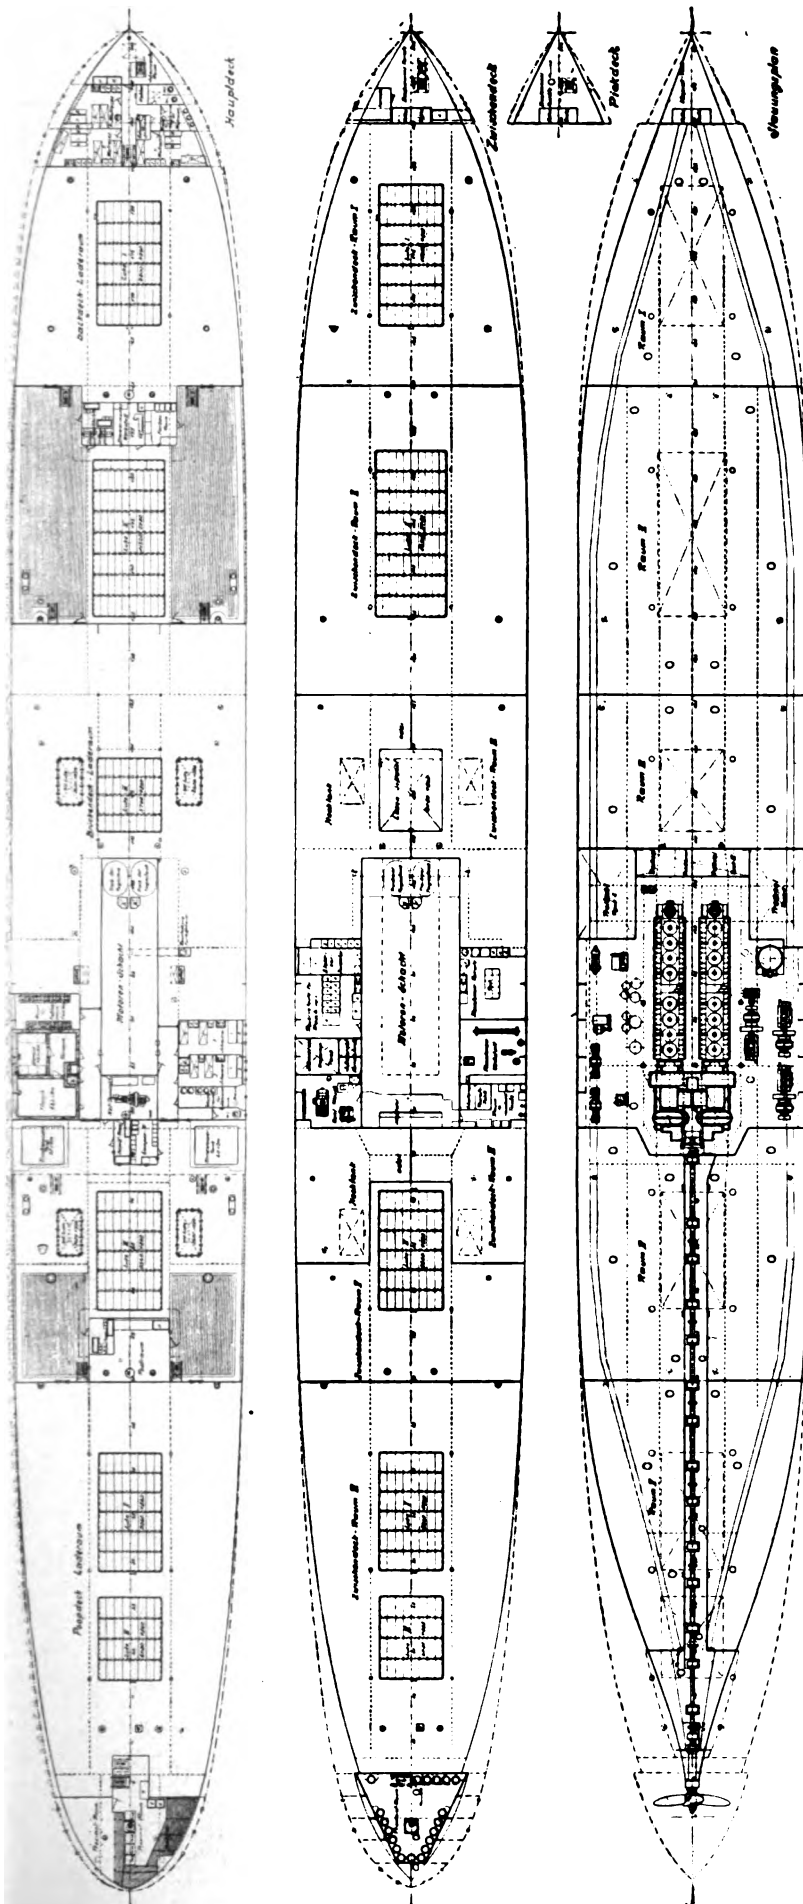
Einschrauben-Motorfrachtschiff „Altenfels“, Maßstab 1:600
